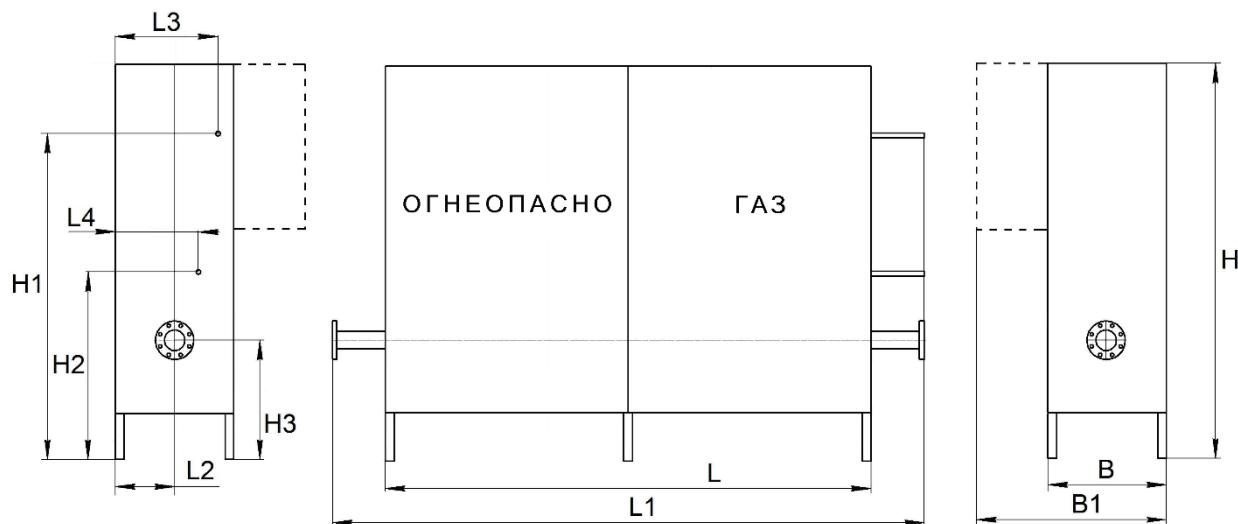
Габаритные размеры [ПУГ](#)
